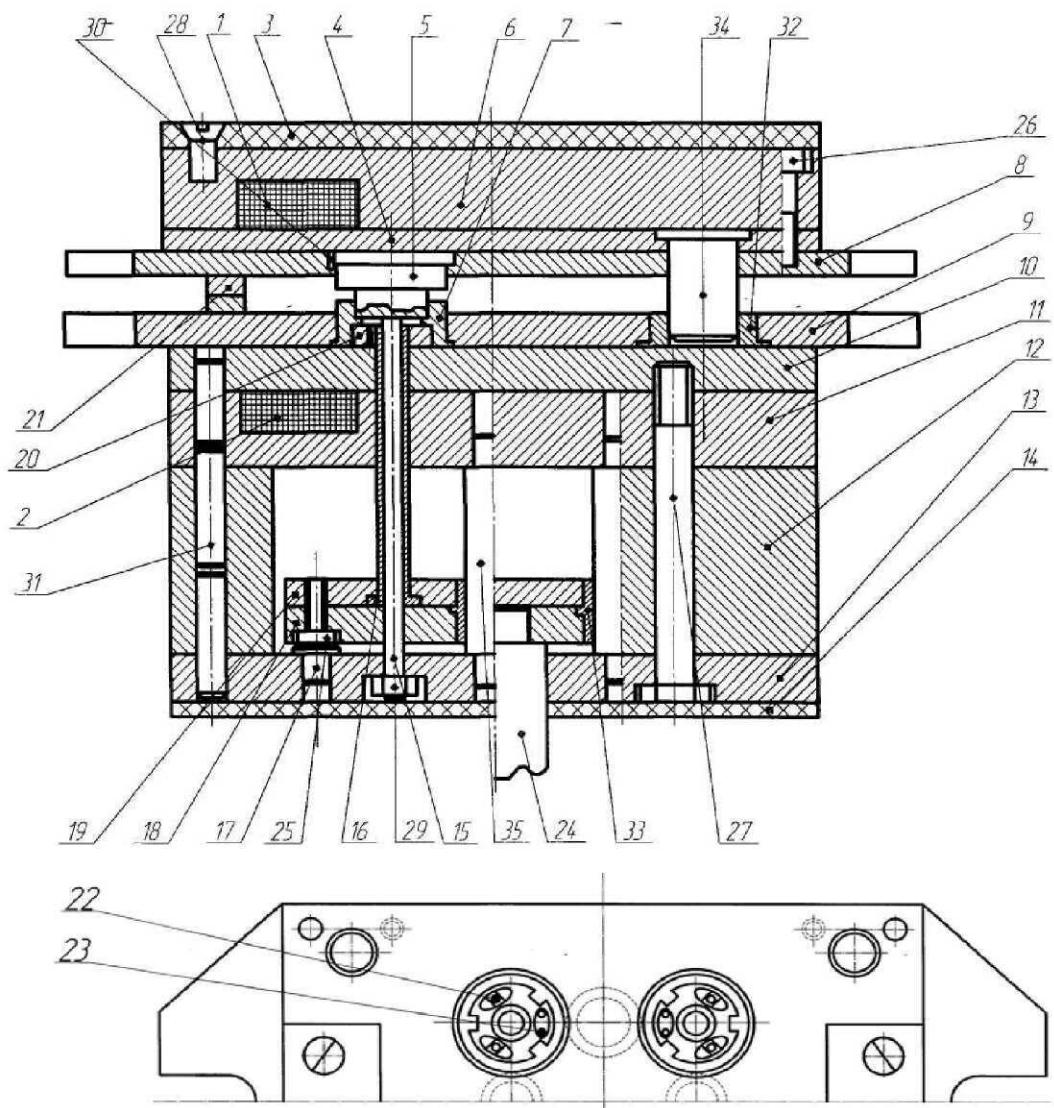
Пресс-форма съемная для изготовления деталей методом литьевого прессования:
